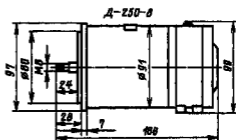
16 Габаритные и установочные размеры двигателя Д-250-8
